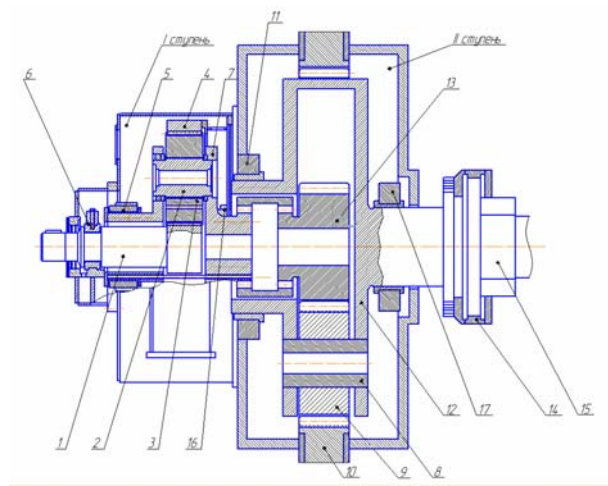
Планетарный редуктор существующей конструкции: 1 - вал-шестерня I ступени; 2,8 - ось сателлита; 3,9 - сателлит; 4,10 - зубчатый венец; 5,11,16,17 - подшипники скольжения водила; 6 - подшипник скольжения вала-шестерни I ступени; 7,12 - водило; 13 - солнечная шестерня II ступени; 14 - зубчатая муфта; 15 - промвал
